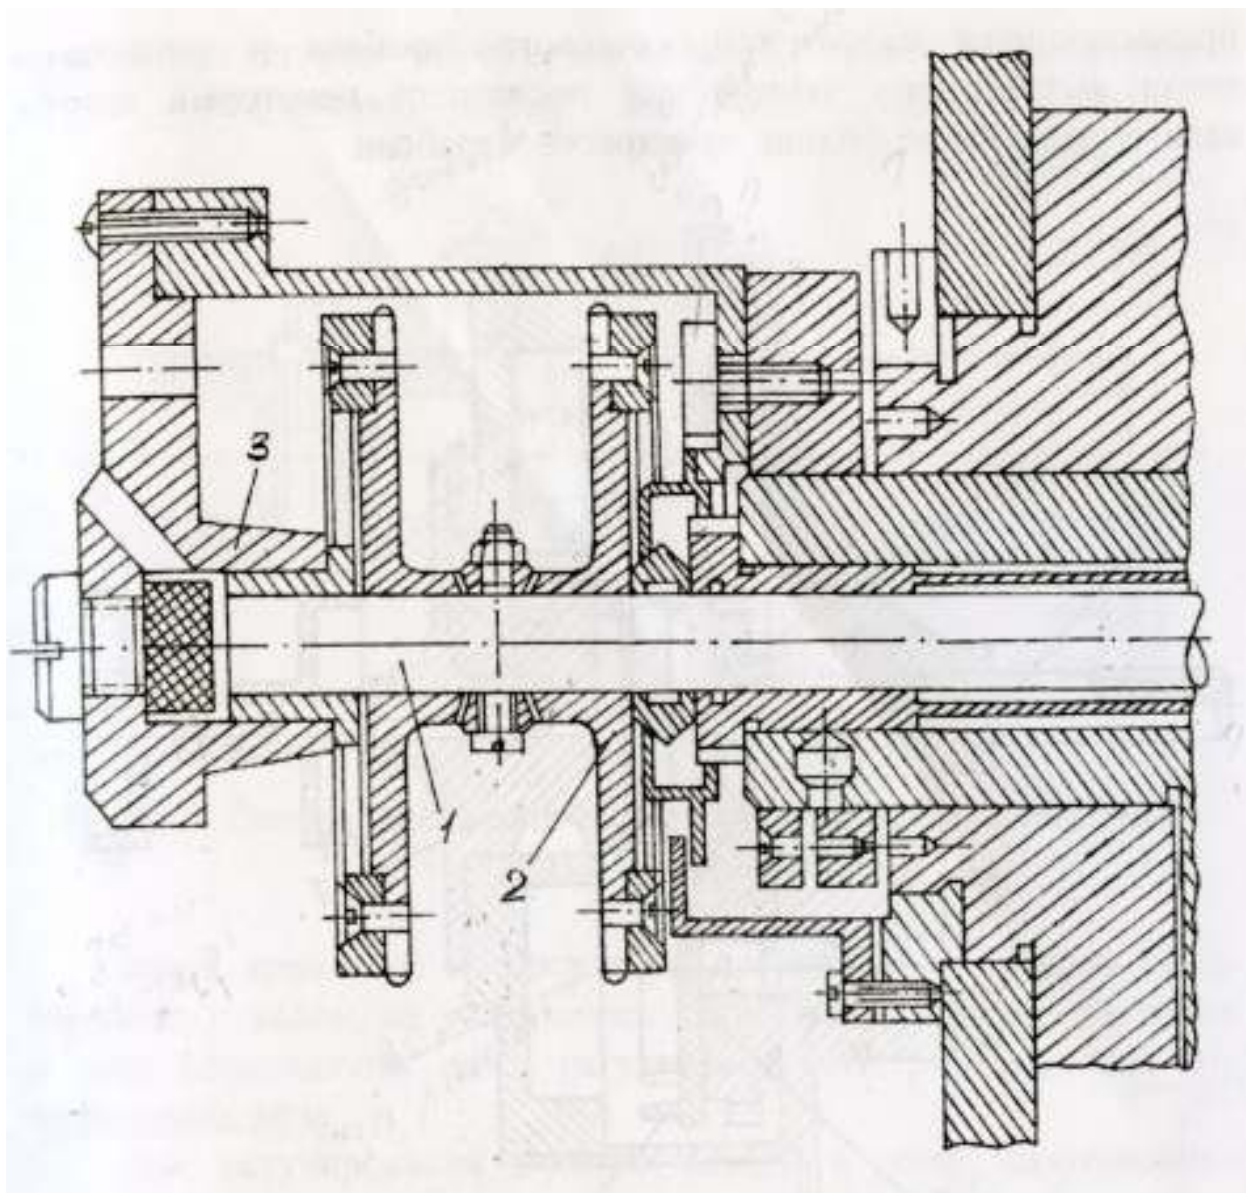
Конструкция мальтийского механизма с двумя опорами вала скачкового барабана:
